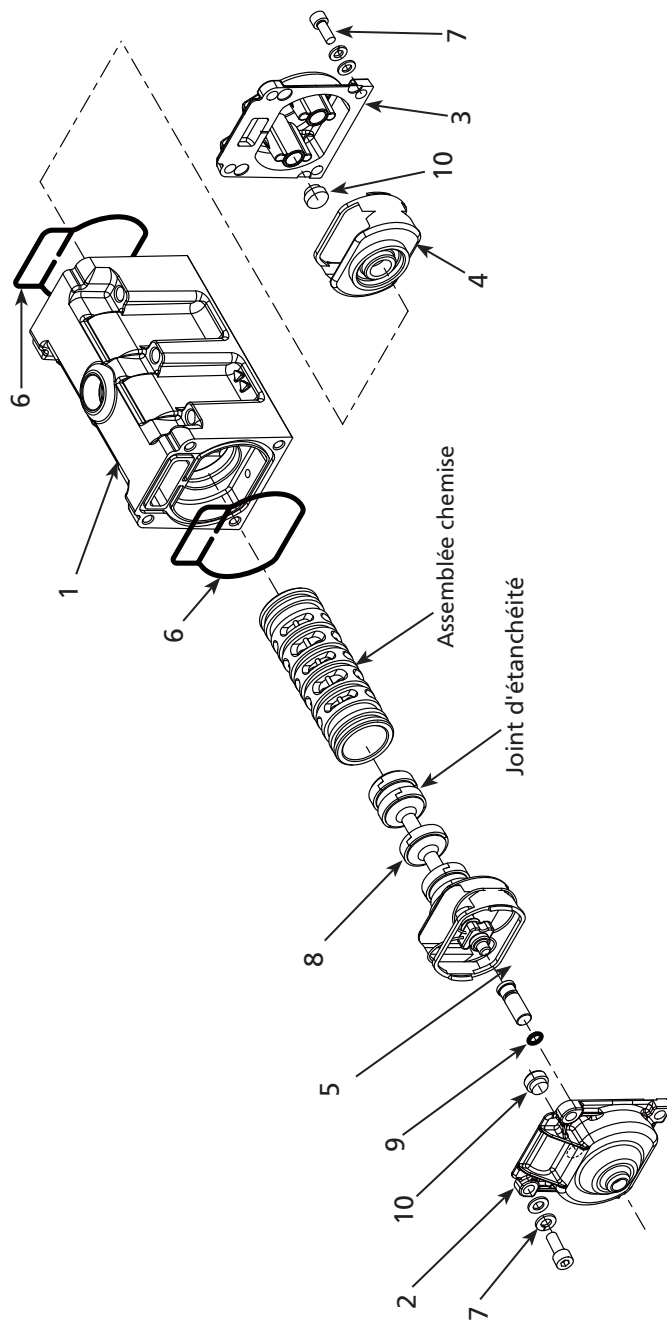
Illustration des pièces de réparation pour Air Valve Assemblée
